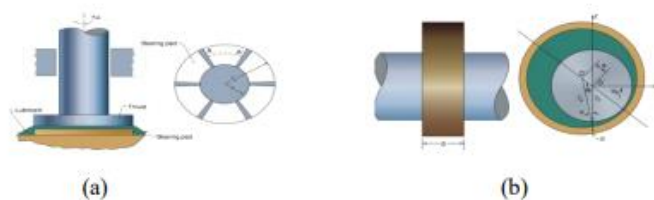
17 kontruksi bearing (a) slider bearing (b) roller bearing
